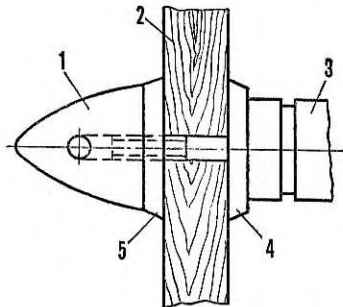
Установка воздушного винта: 1 — кок винта, 2 — винт, 3 — двигатель, 4 — упорная шайба, 5 — шайба.
